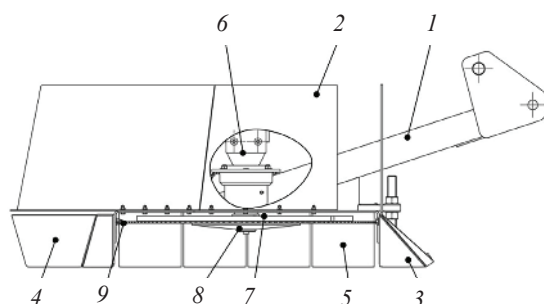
Рабочий орган: 1 – рама; 2 – кожух; 3 – полоз; 4 – полоз; 5 – фартук; 6 – привод;
